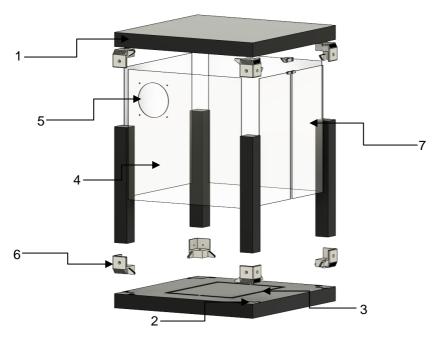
, 22.12.2021, Explosionsansicht Gehäusesystem
